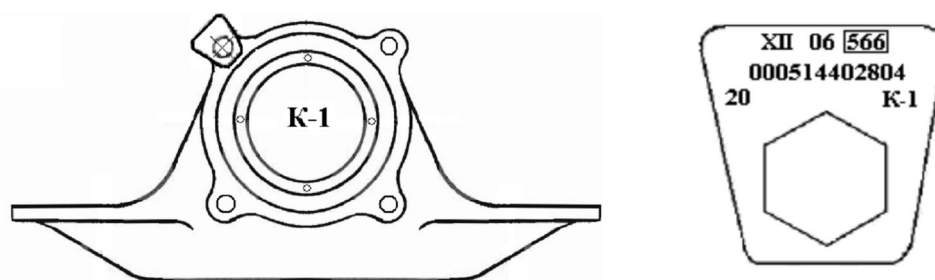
Внешние отличительные признаки буксовых узлов с подшипниками кассетного типа в габаритных размерах 130x250x160 мм торговой марки Бренко
